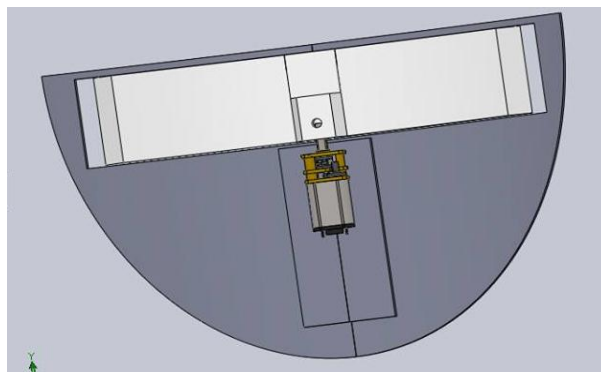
Acople del Motor al mecanismo para patear diseñado en SolidWorks
